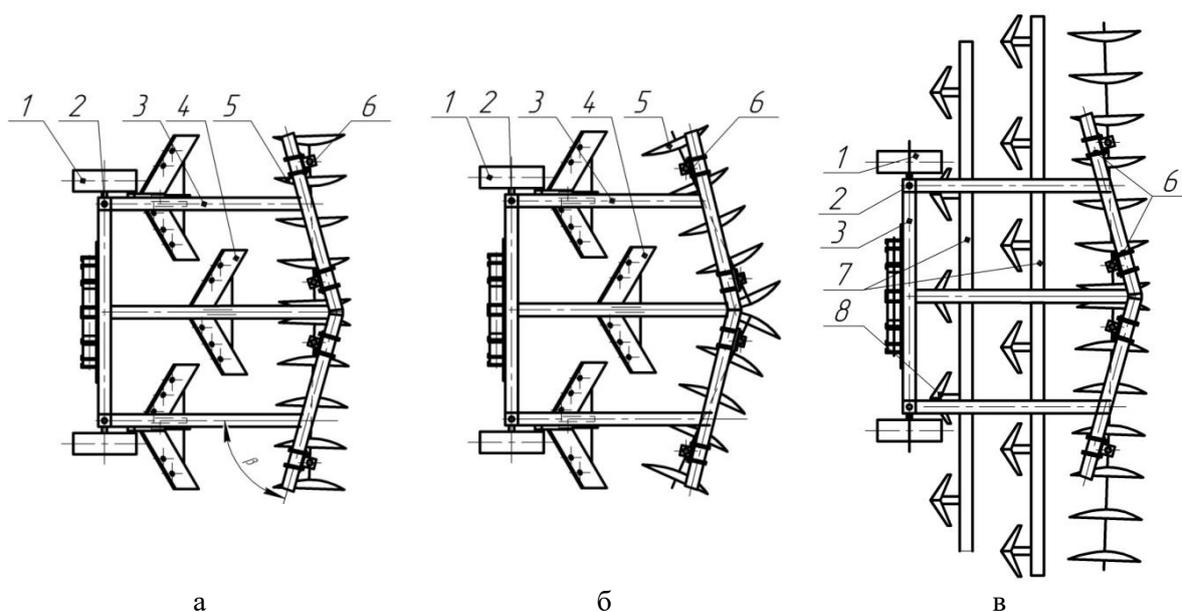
Схема размещения рабочих органов почвообрабатывающего агрегата (плоскорезящие лапы установлены по схеме «обратного» клина):
